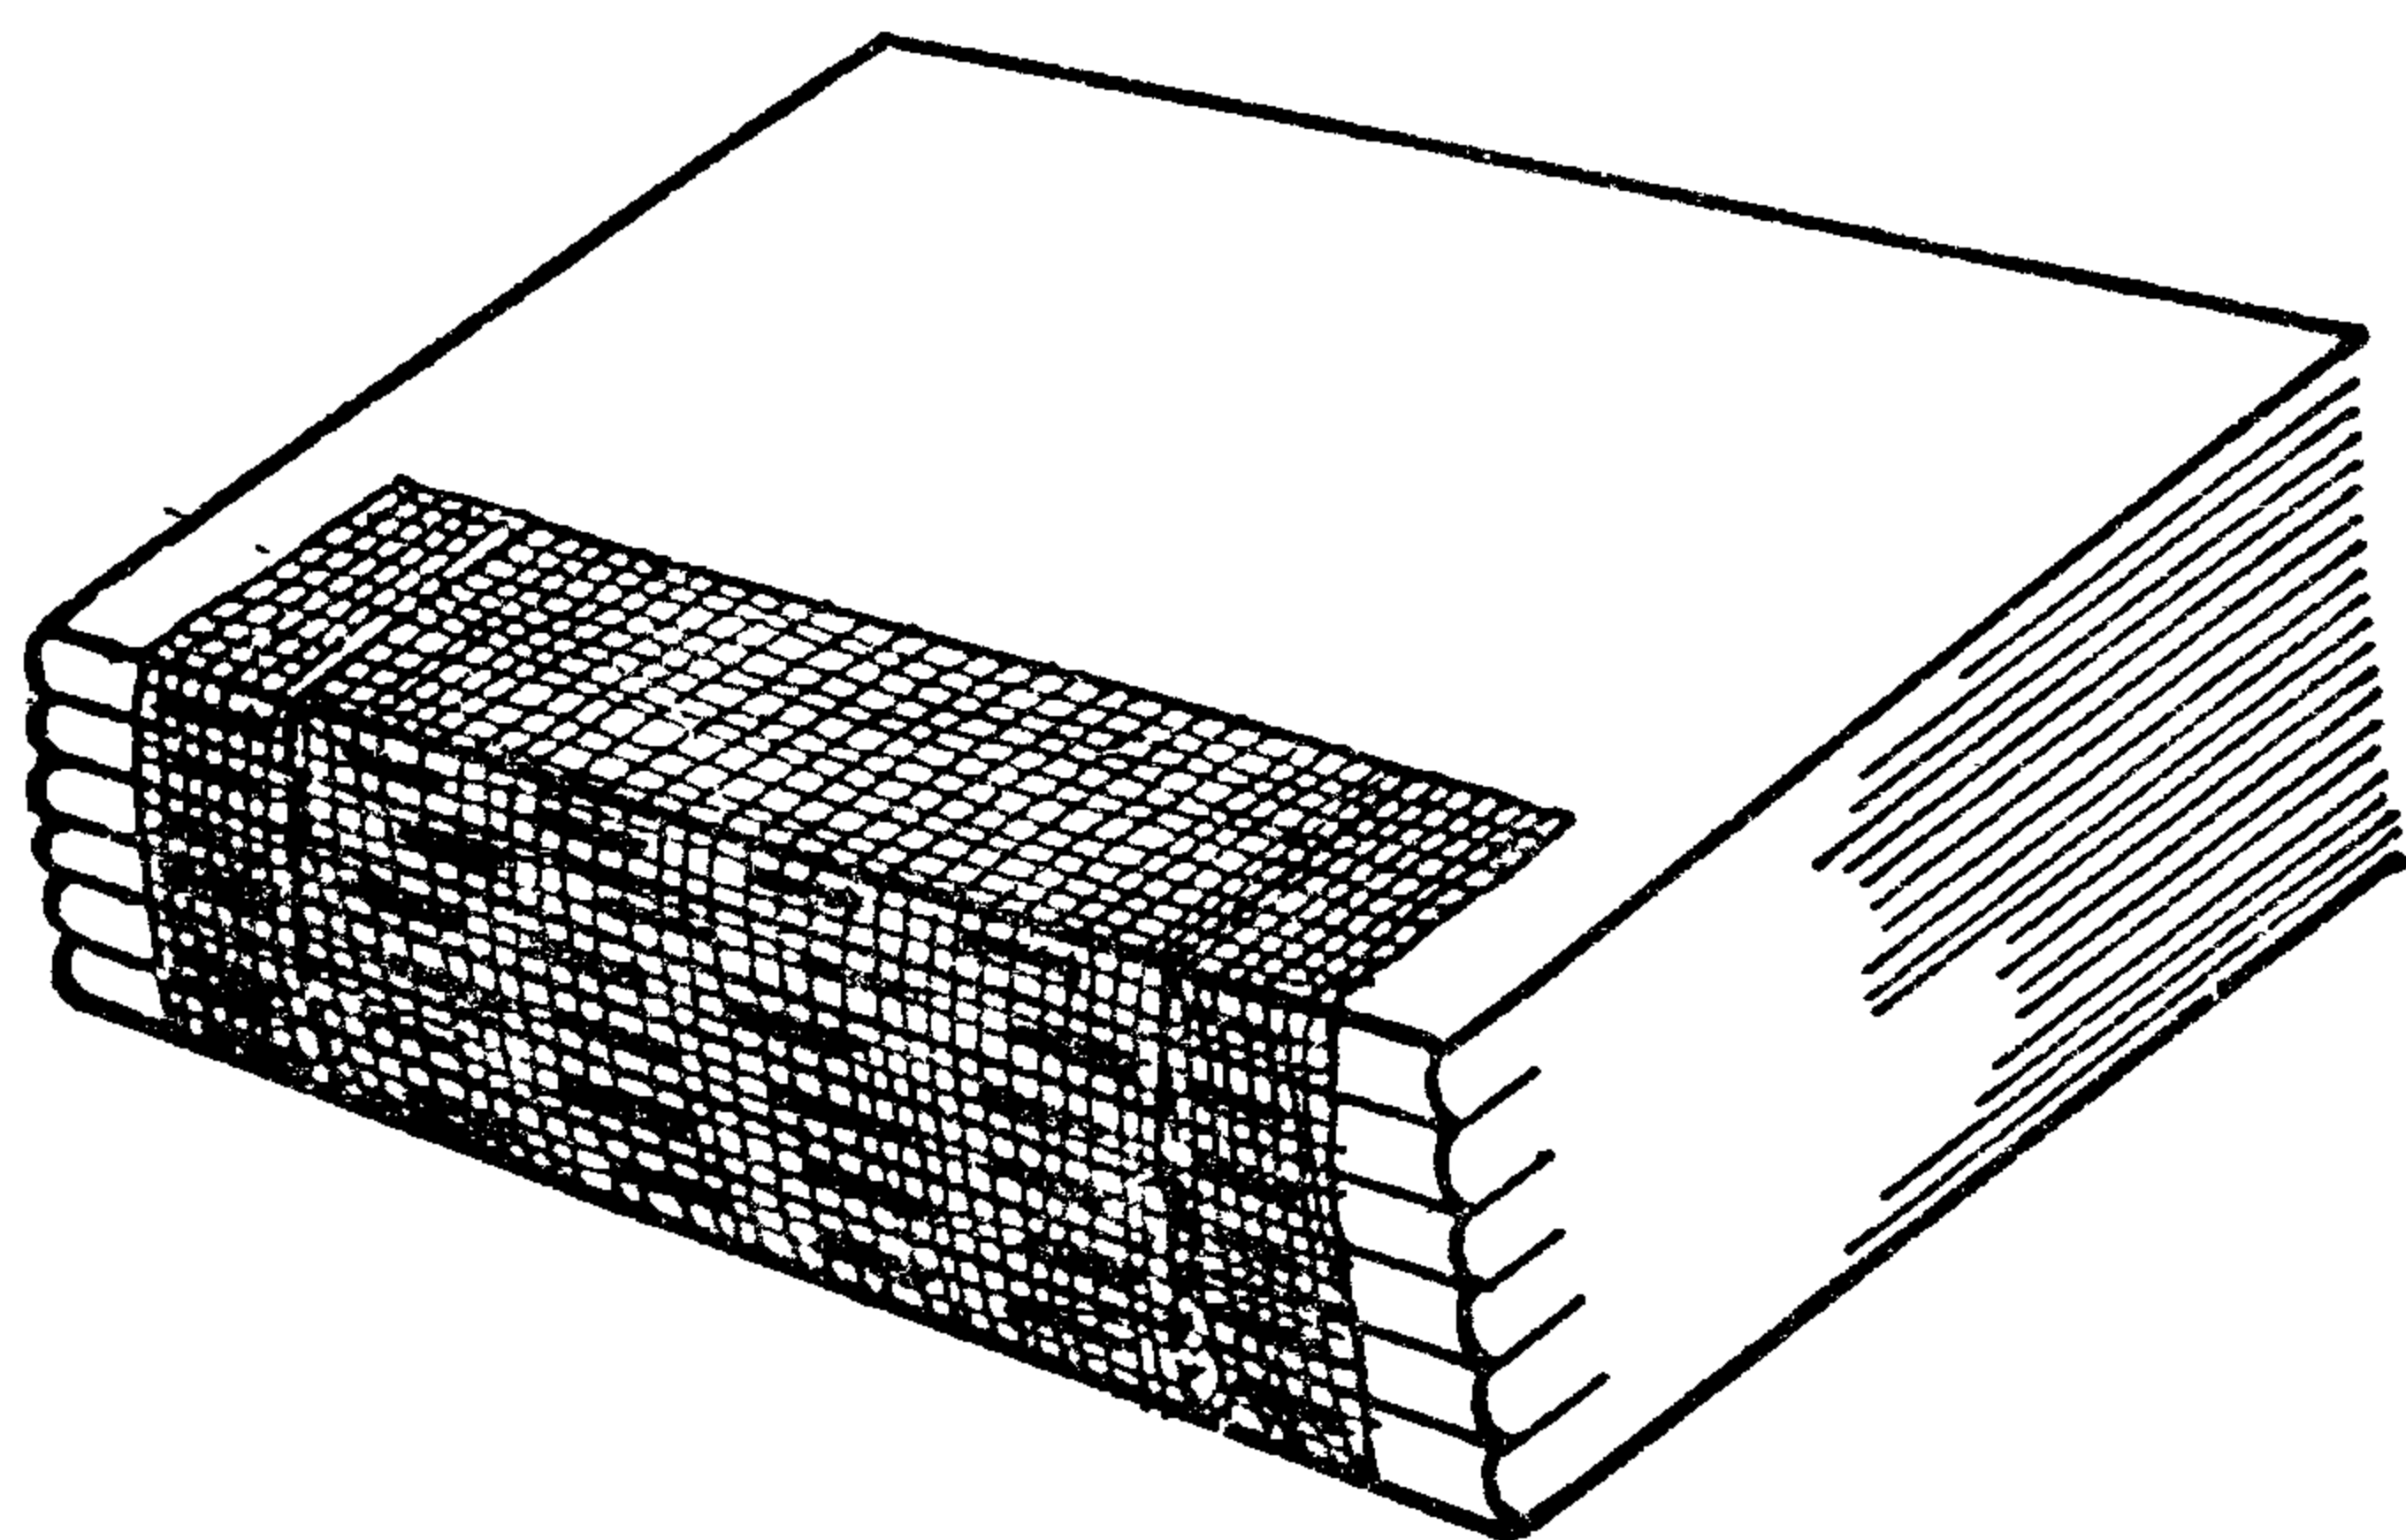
Прошивка (укрепление) корешка книжного блока.
